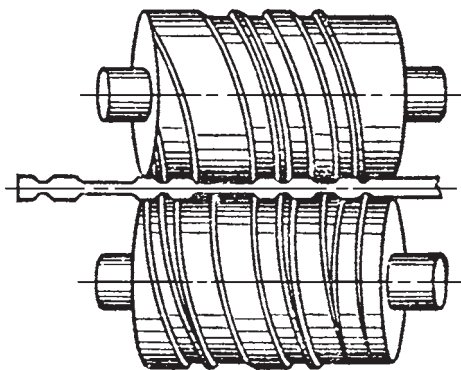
Схема прокатки заготовки для штамповки шатуна
